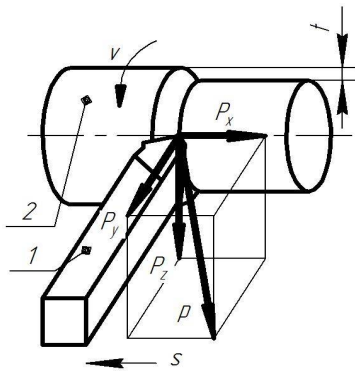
Складові сили різання: 1 – різець; 2 – заготовка
